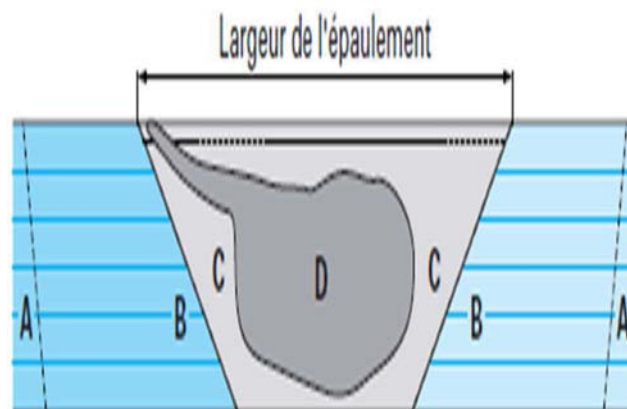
Coupe transversale schématisée d'une soudure
